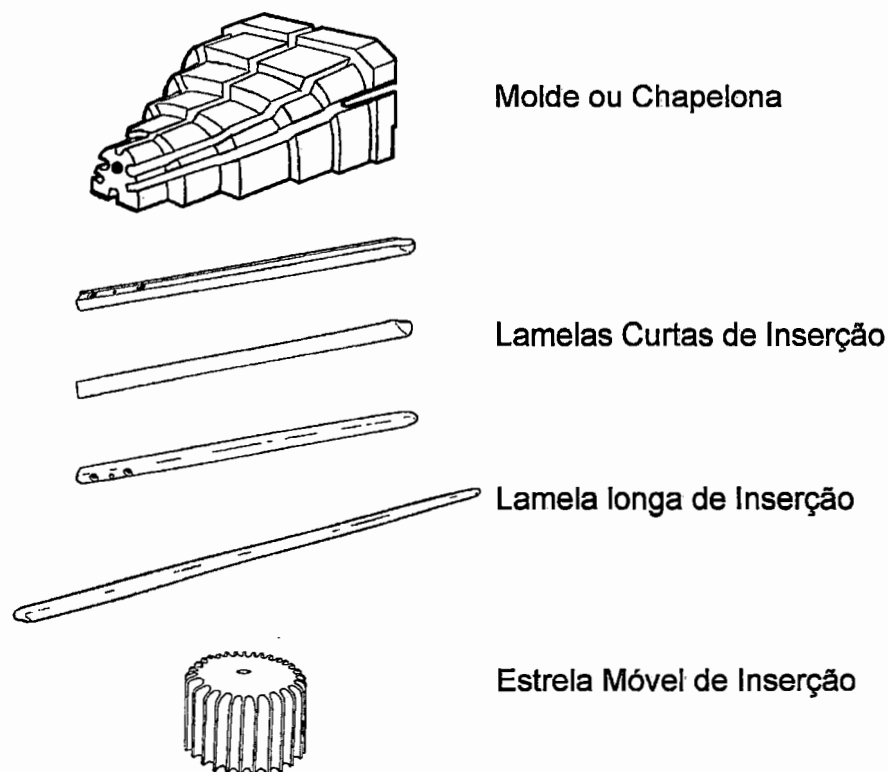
Ferramentas para máquinas de bobinagem e inserção de estator
